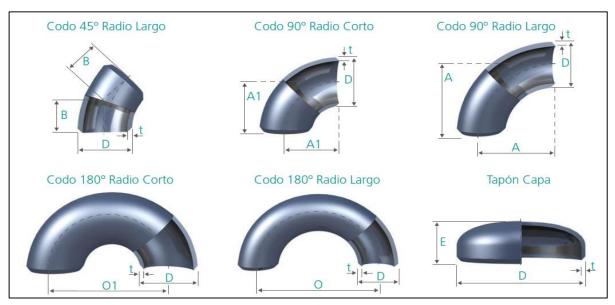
tipos de accesorios de acero para soldar a tope.
